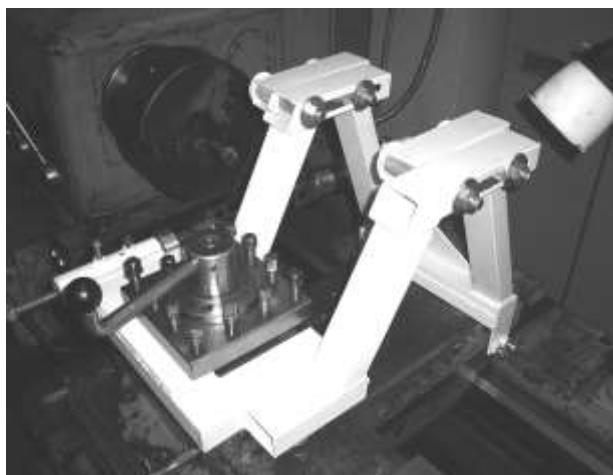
Приспособление для резания с ОПД встречно-направленного действия
